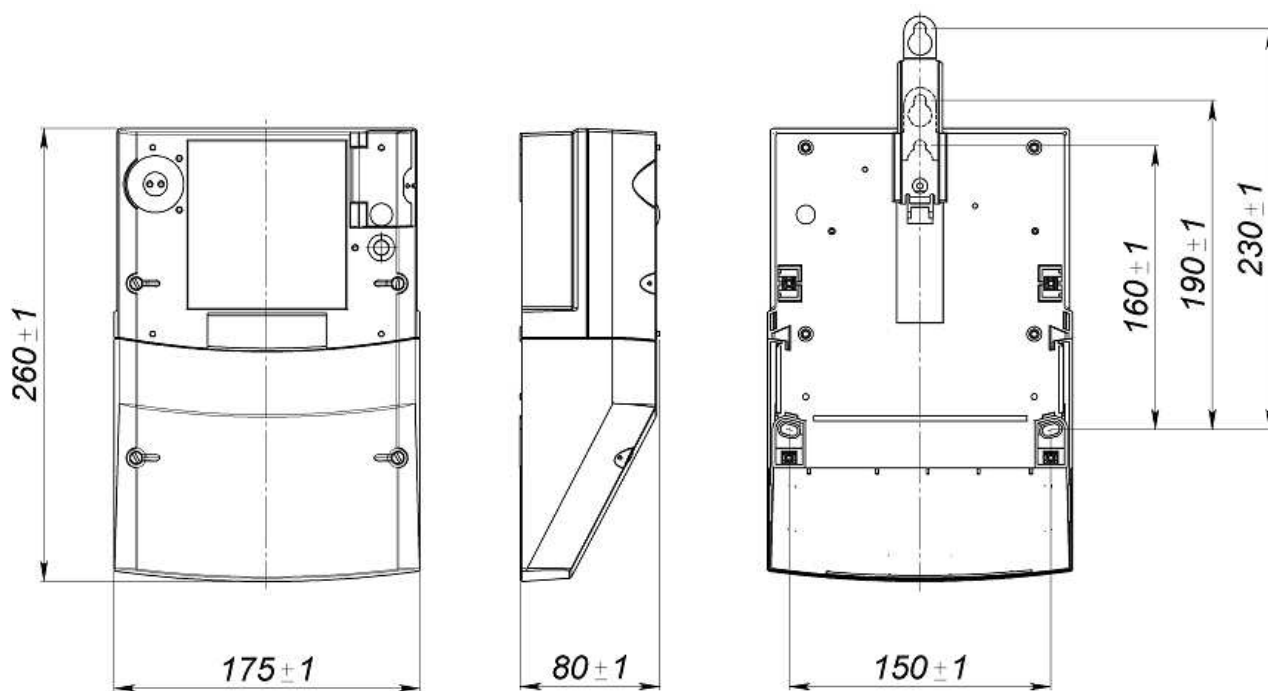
Габаритные размеры счетчика и расположение отверстий для крепления
